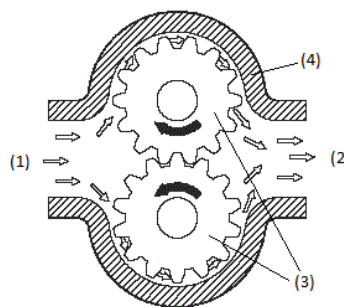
Bomba hidráulica de engrenagens com dentado exterior. Adaptado de (7)
